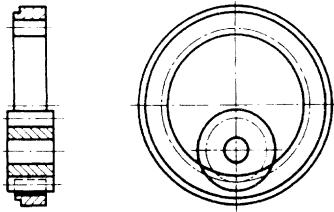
Stirnrad mit innenliegendem Gegenstand
